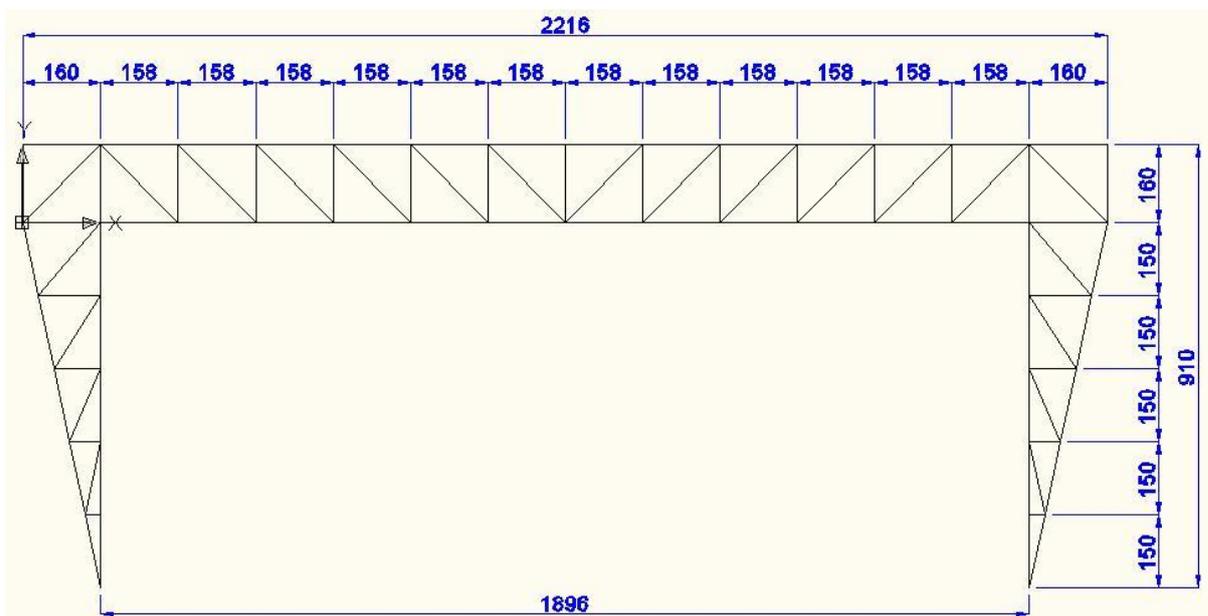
Vista frontal e dimensões da ponte rolante (em cm).
